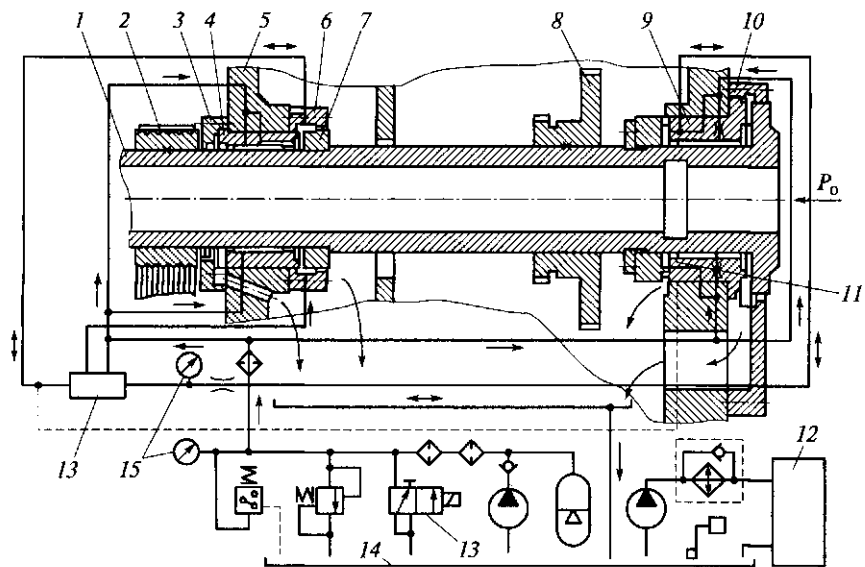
Шпиндельный узел с гидростатическими опорами:
